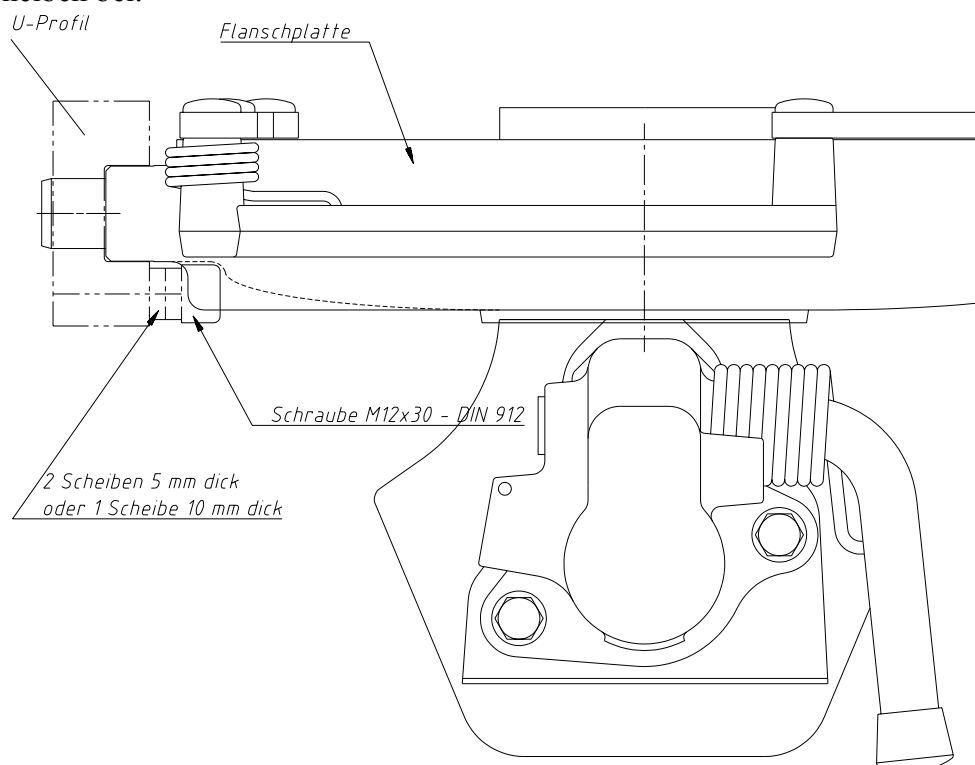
Neue Flanschplatte mit neuer Stopperschraube
